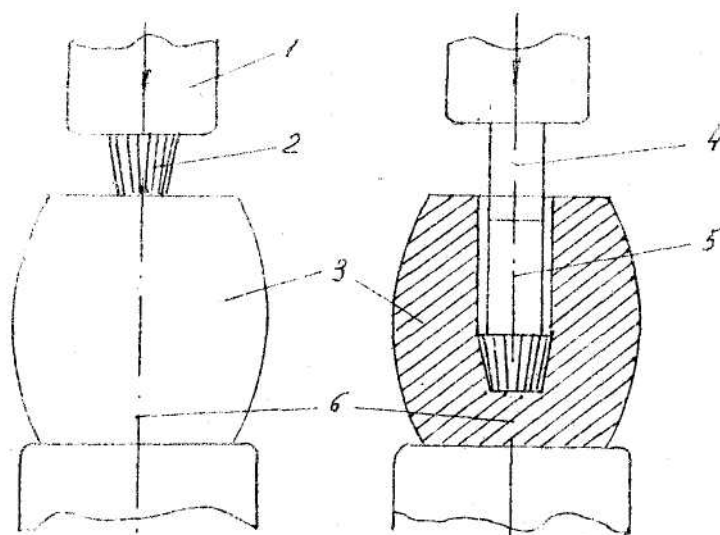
Схема прошивки: 1 - верхний боек; 2 - основной прошивень; 3 - заготовка; 4 и 5 - надставки; 6 - прибыльная сторона слитка
